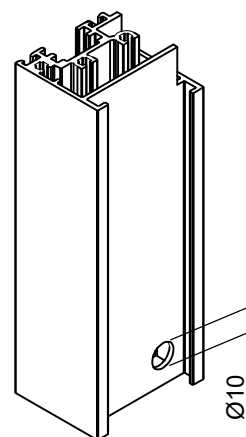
x 45. Povezivanje vertikalnog pojasa rama F-1600 i praga F-1612
